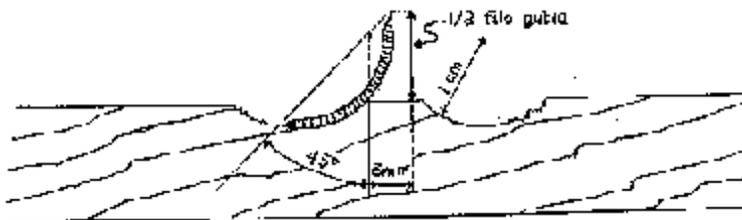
Forma de Corte Oblicuo para Ensayo de Torneado
